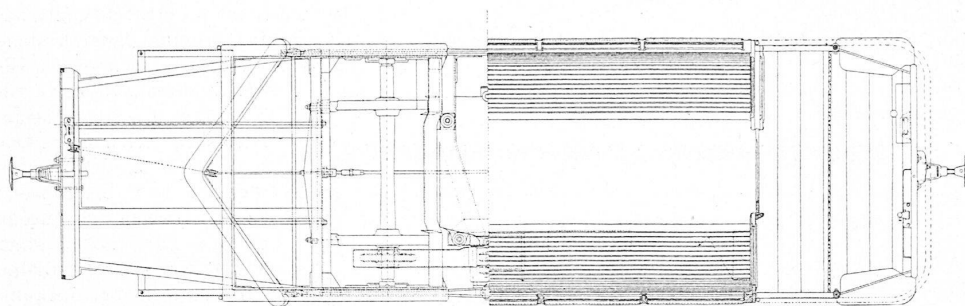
Horizontalschnitt und Grundriss.
